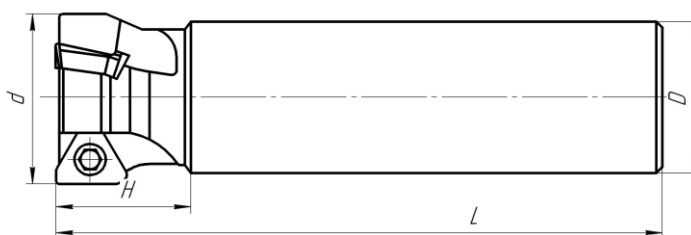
Кінцева фреза НМ390 ЕТС D18-2-W20-07
